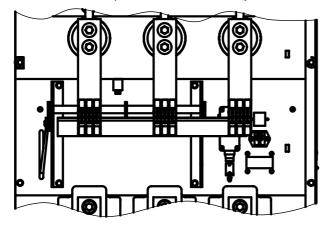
Узел заземления для шкафов с верхним расположением сборных шин
